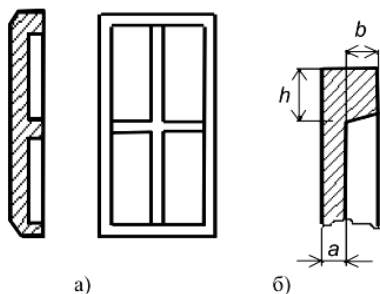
Конструкция литых деталей. снижающая коробление отливко
